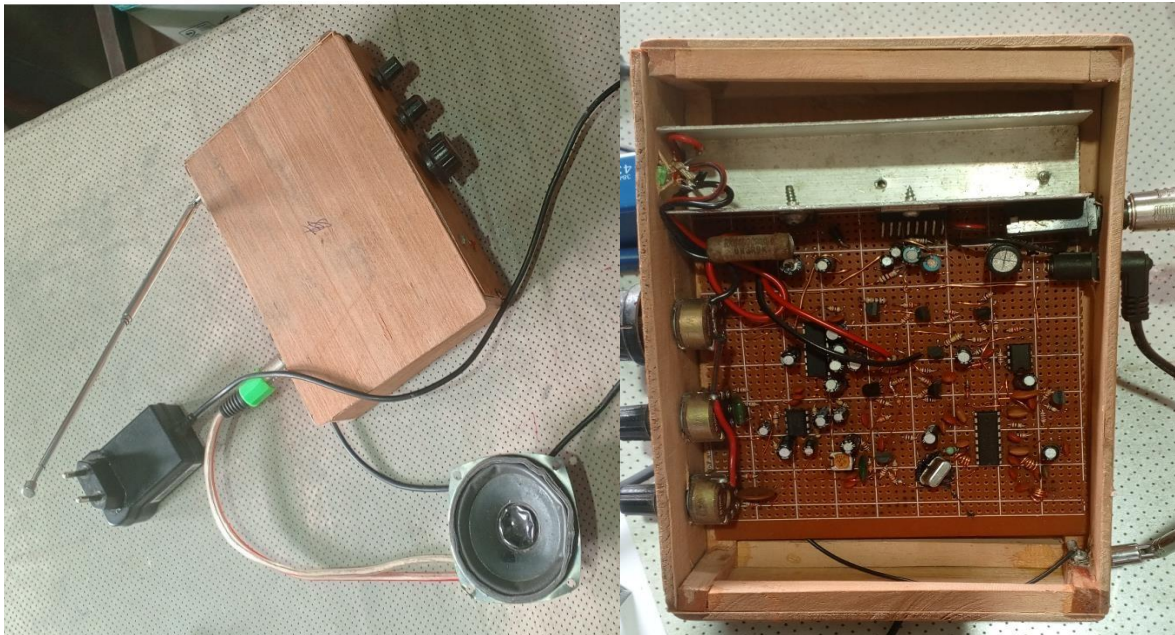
Le montage de récepteur par soudure avec fer à souder et étain
